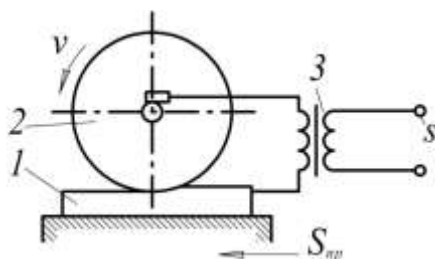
Схема електроконтактної обробки плоскої поверхні: 1 – оброблювана заготовка; 2 – інструмент – електрод; 3 – трансформатор.
